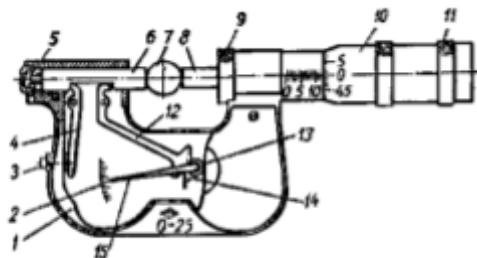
Важільний мікрометр: 1 – скоба; 2 – шкала; 3 – кнопка; 4 – важіль; 5 – пружина; 6 – п'ятка; 7 – виріб; 8 – мікрометричний гвинт; 9 – стопорний пристрій; 10 – барабан; 11 – ковпачкова гайка; 12 – важіль; 13 – зубчасте колесо; 14 – спіральна пружина; 15 – стрілка
